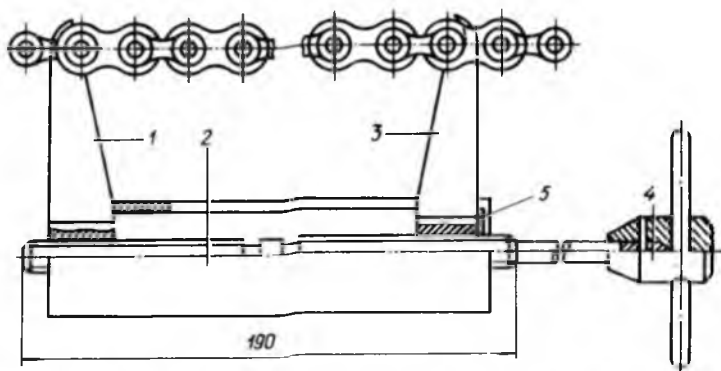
Струбцина для стягивания втулочно-роликовых цепей при их разъединении и соединении:
